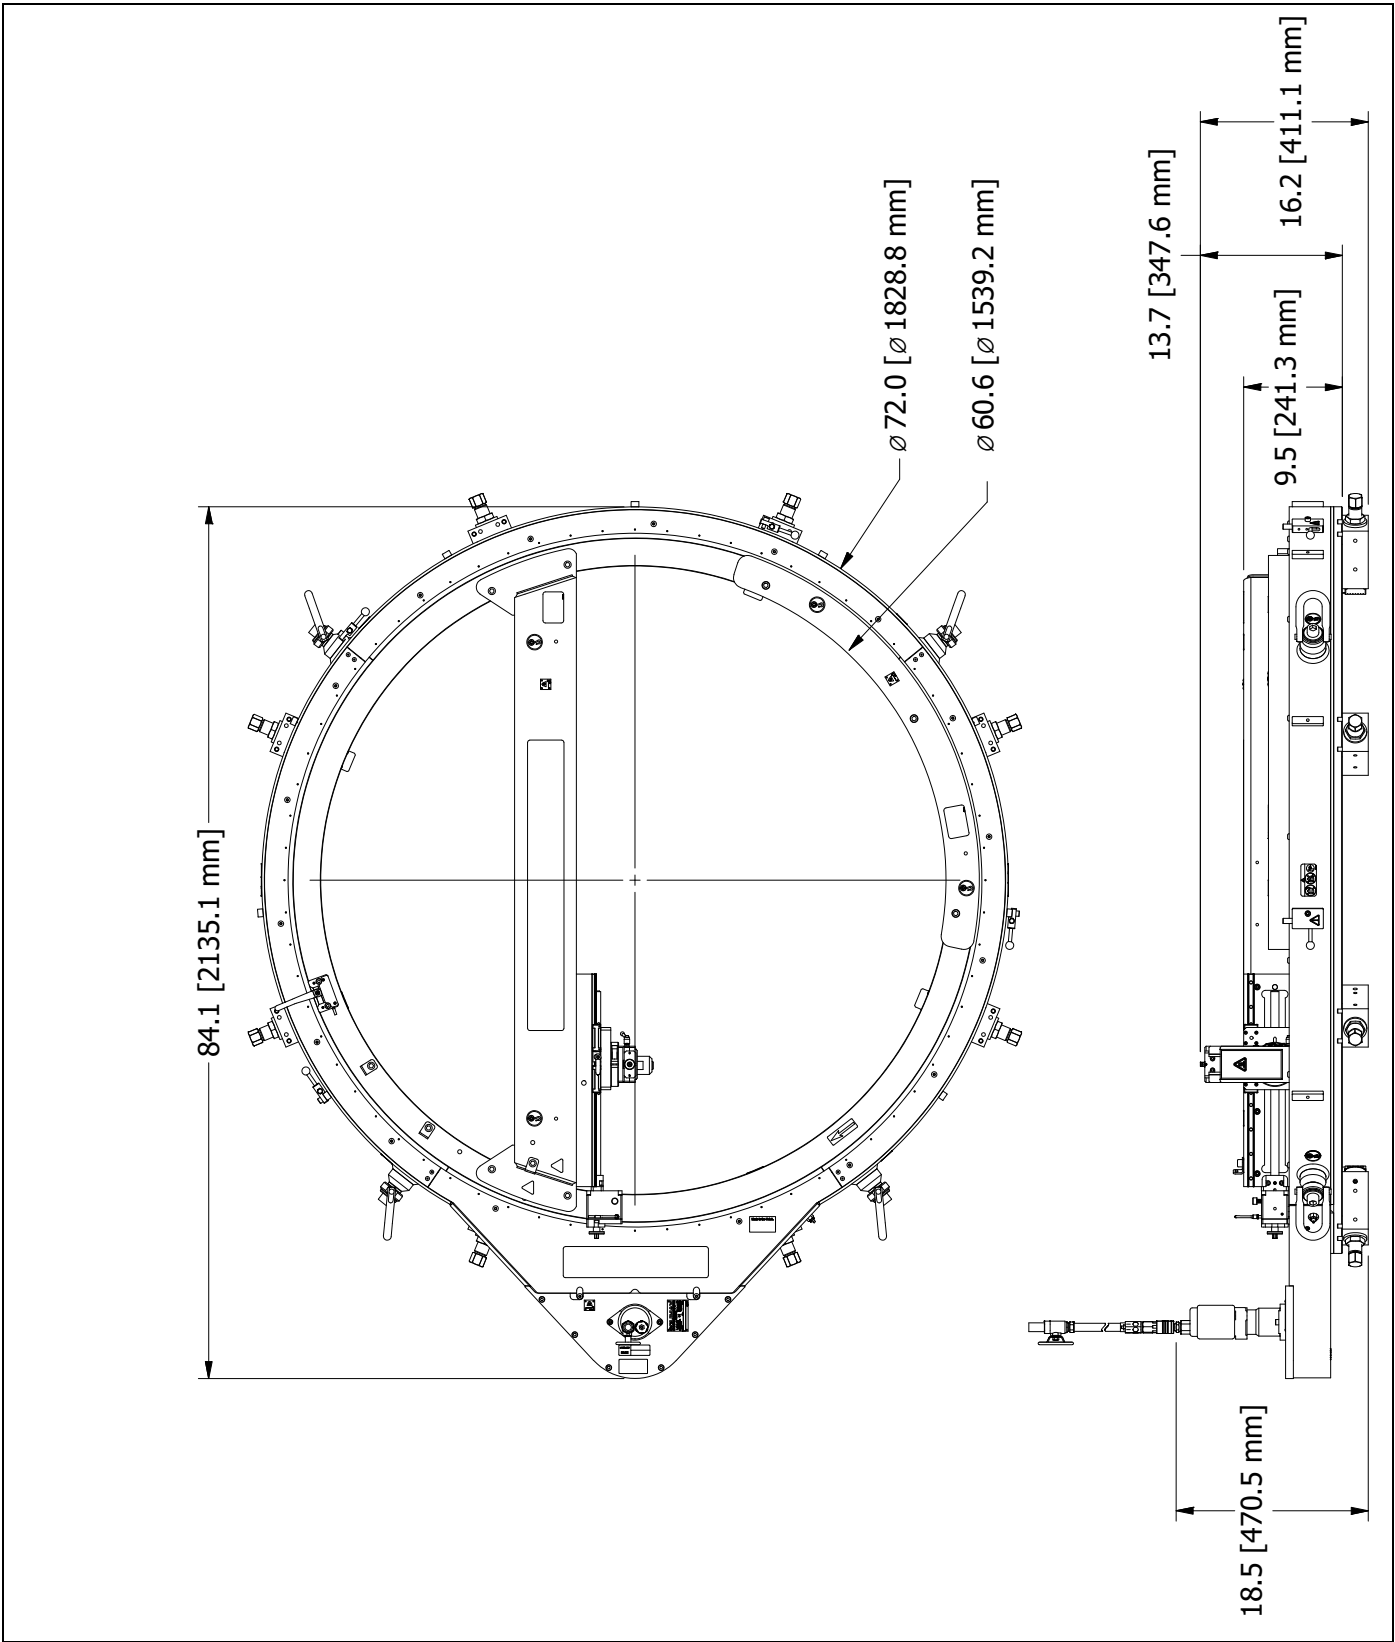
DIMENSIONES DE LA ODF60 SPEED FACER (N/P 86990)
